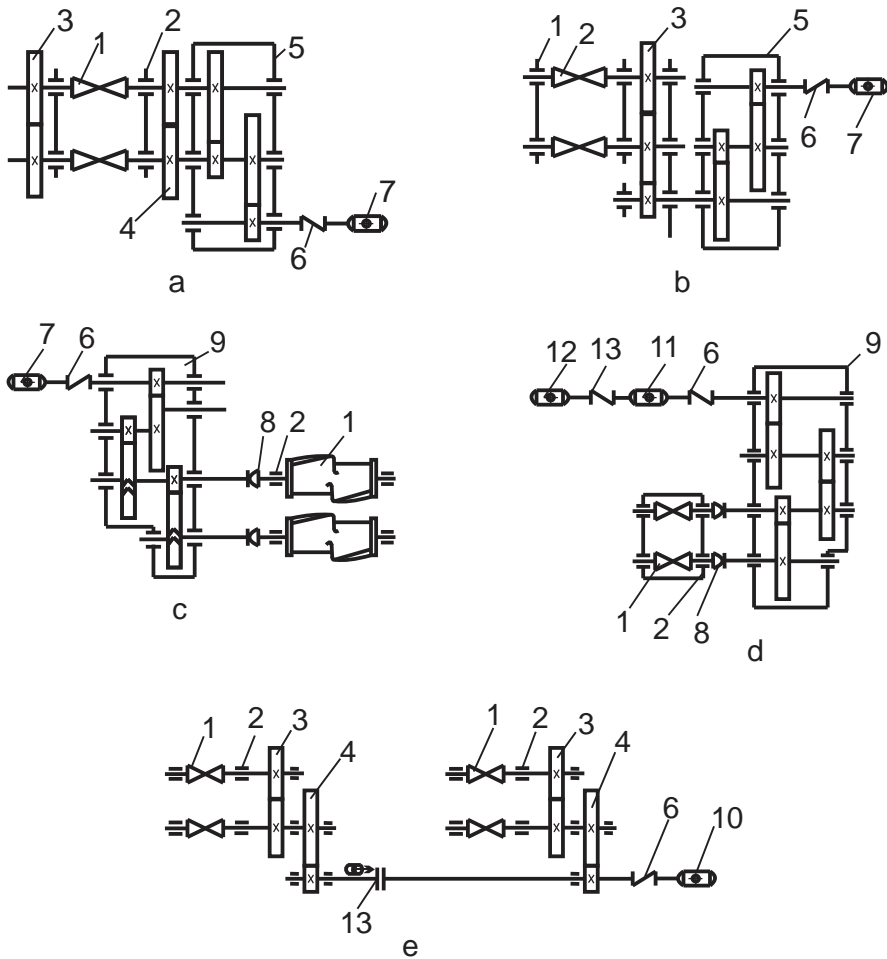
Scheme de acționare a malaxoarelor cu rotoare. 1 – rotoare; 2 – lagăre; 3, 4 – roți dințate; 5 – reductor cu roți cilindrice; 6 – cuplaj elastic; 7 – motor de curent alternativ; 8 – cuplaj sferic; 9 – reductor bloc; 10 – motor sincron; 11 – motor de curent continuu de putere mică; 12 – motor de putere mare; 13 – cuplaj pneumatic automat.
